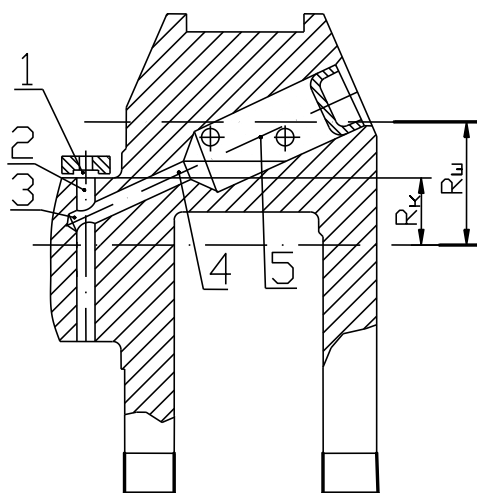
Схема смазки шатунного подшипника двигателя КамАЗ:
